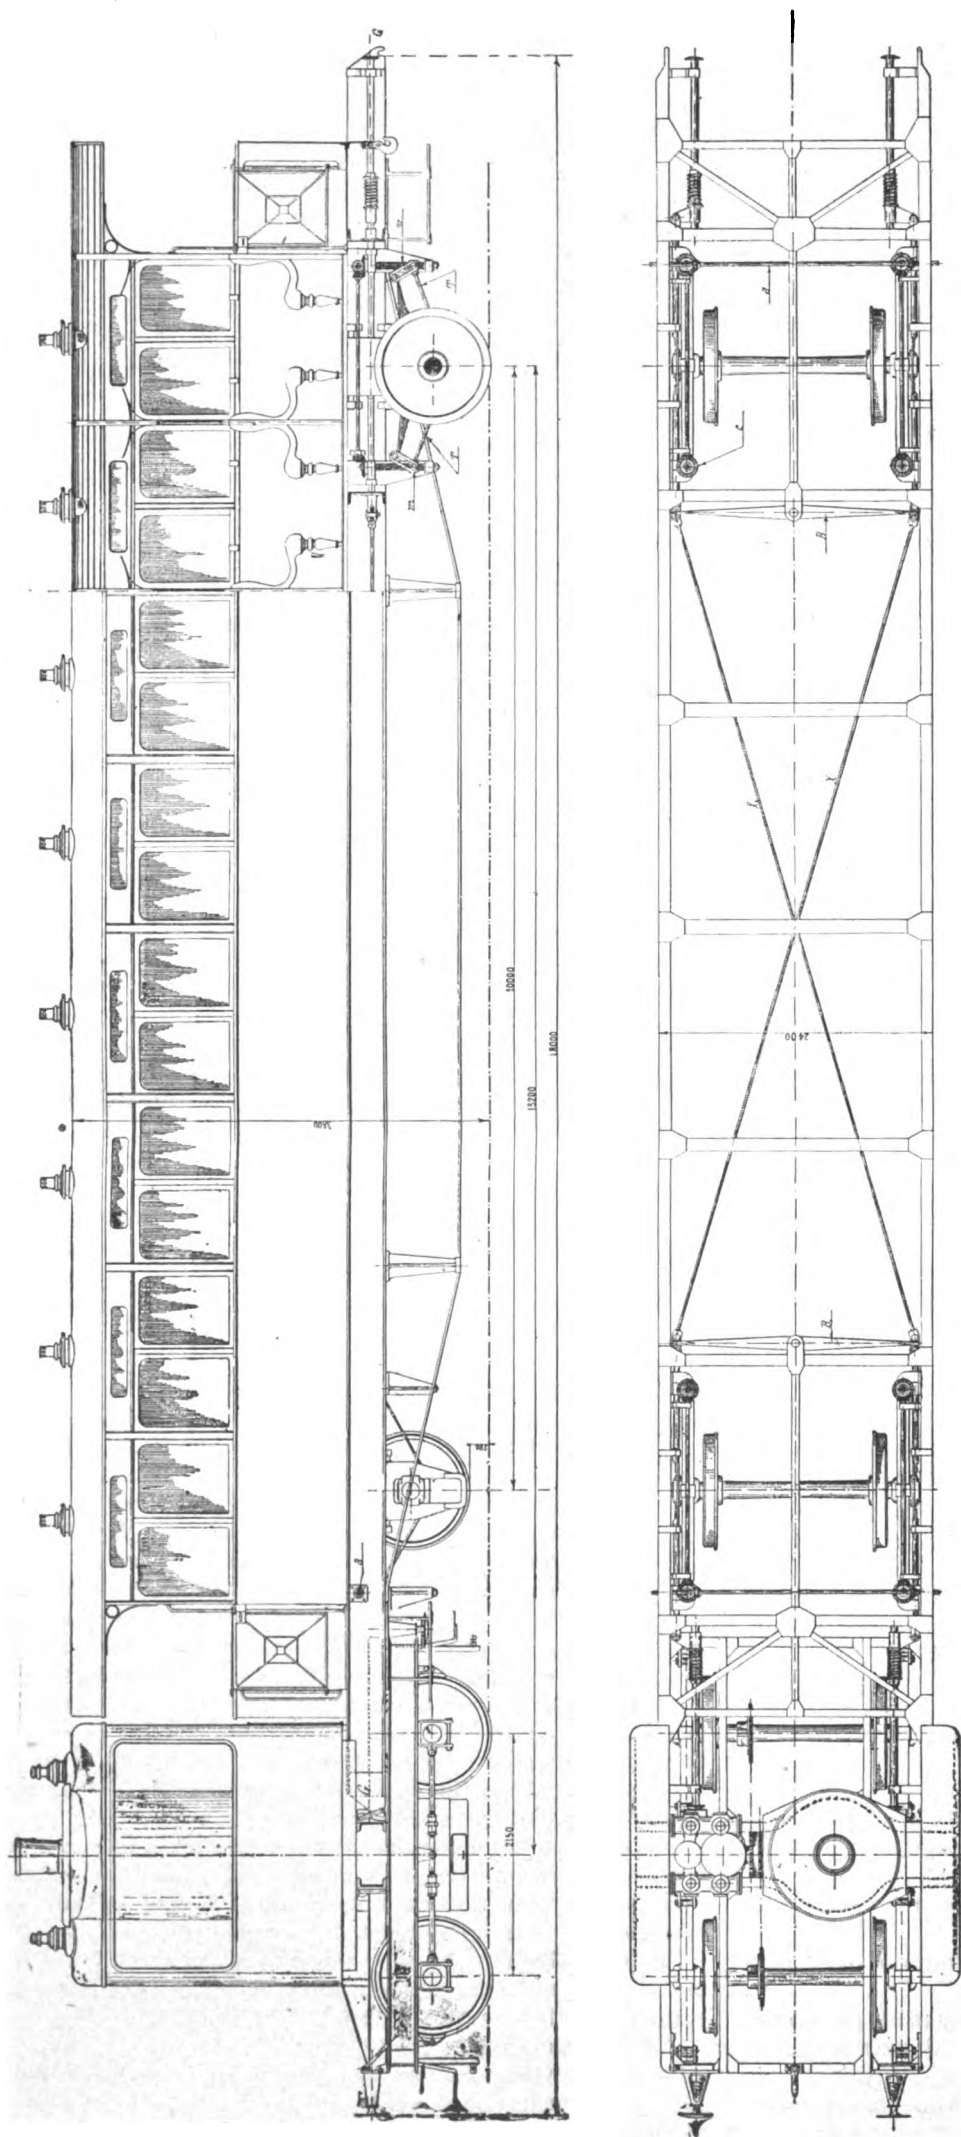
e 12. — Progetto di treni economici. — Prospetto, sezione longitudinale e pianta.
